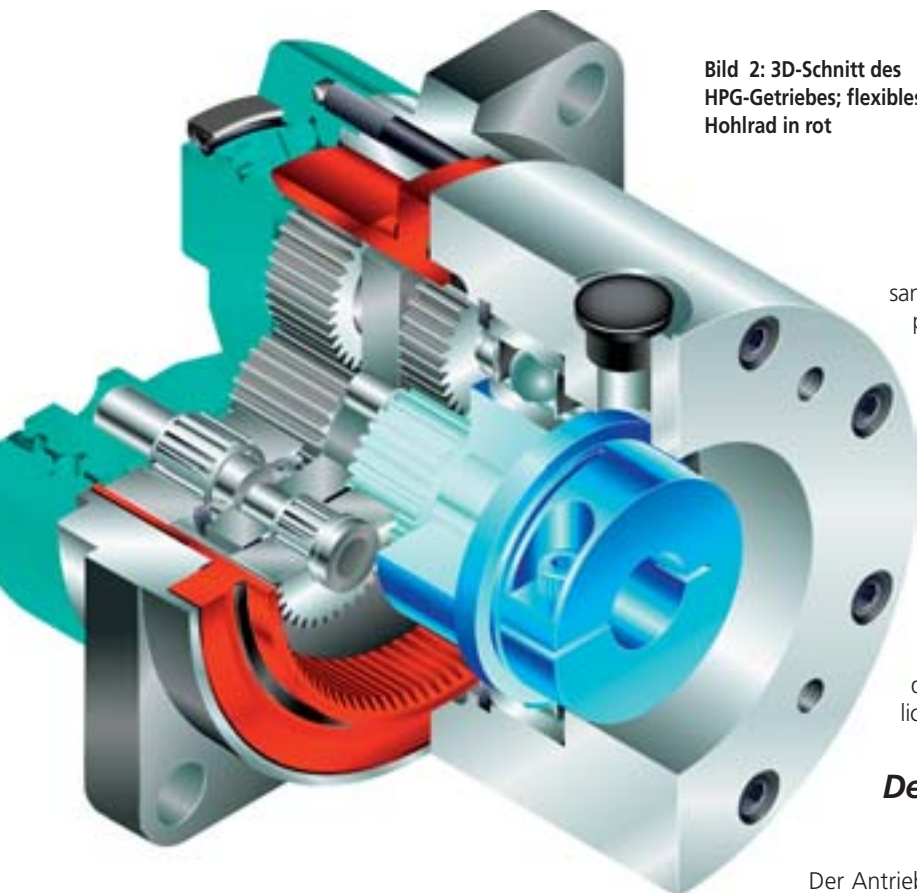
3D-Schnitt des HPG-Getriebes; flexibles Hohlrad in rot
